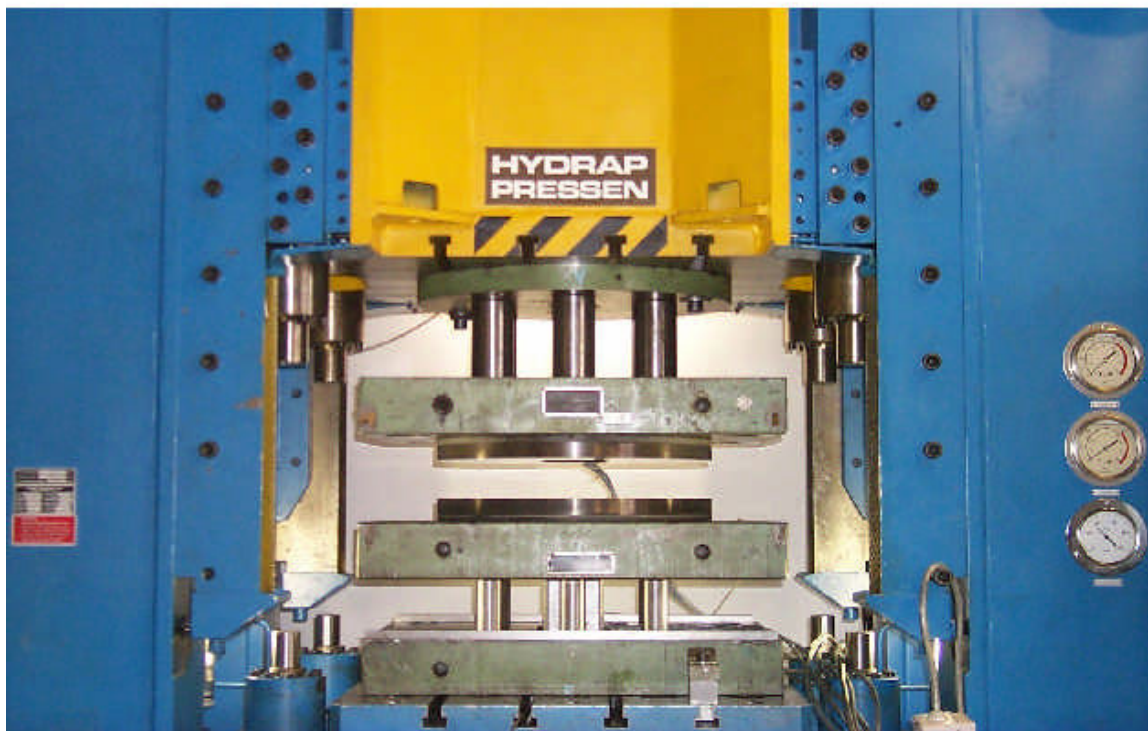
Hydraulische Tiefziehpresse Hydrap HPDZb 63 mit eingebautem beheizbarem Tiefziehwerkzeug (Stempelgeometrie 220 mm x 110 mm)
